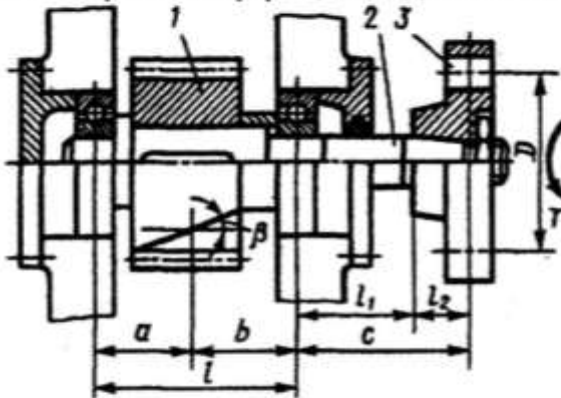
Вал с элементами, расположенными на нем: 1 – шестерня; 2 – вал; 3 – полумуфта
